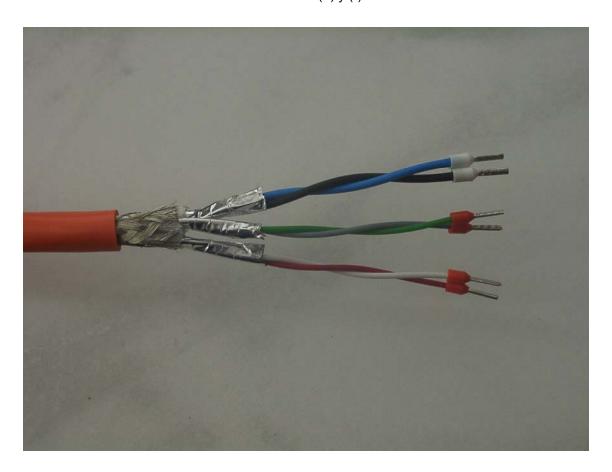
Pares de conductores en los cables con cubierta protectora
